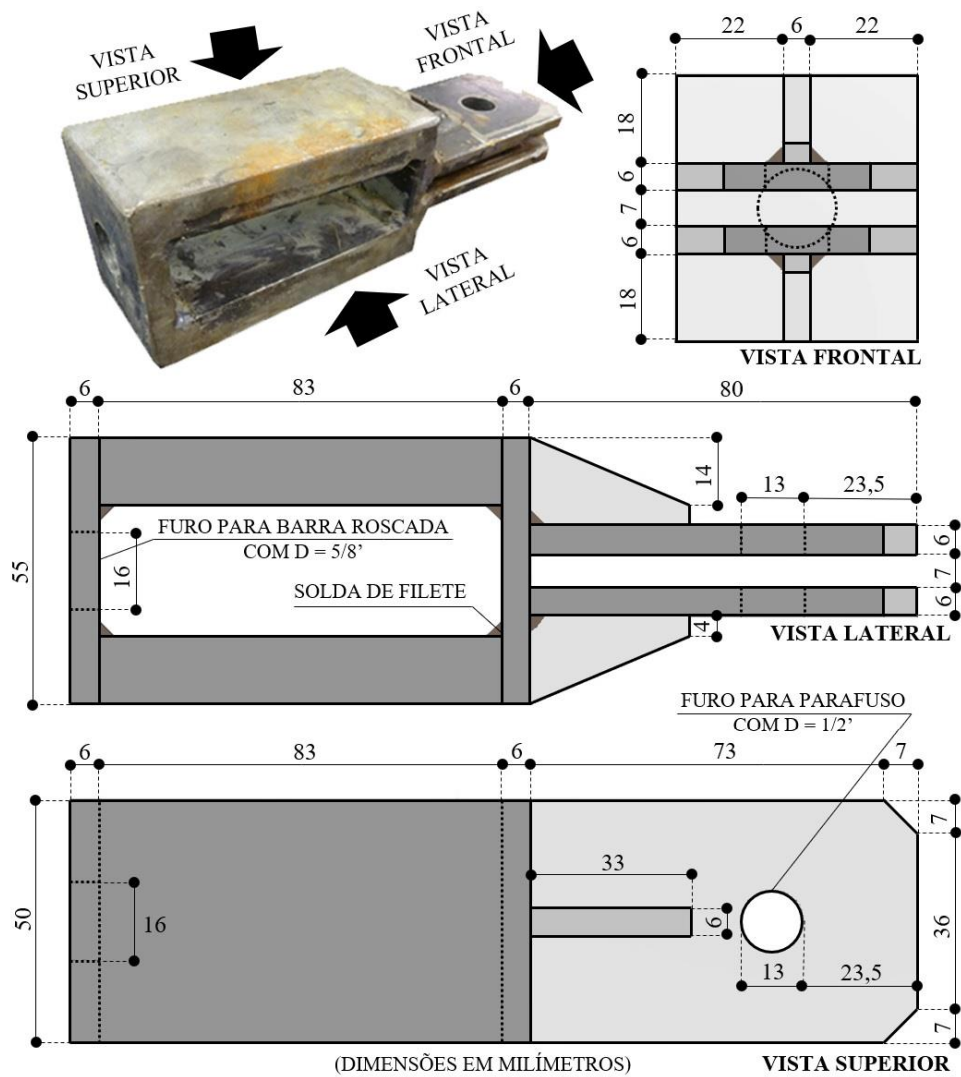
Conexão 1 para ensaios de arrancamento (suporte para reforços metálicos e para conexão 2).
